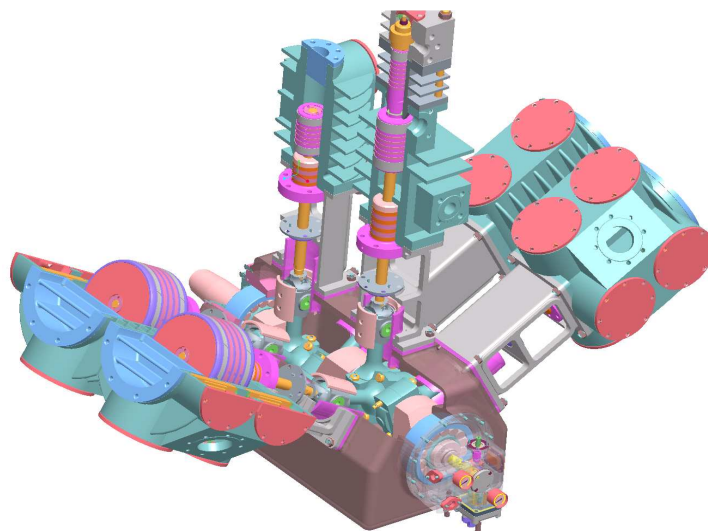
Компрессор W-образный 6ГШ5-40/250
